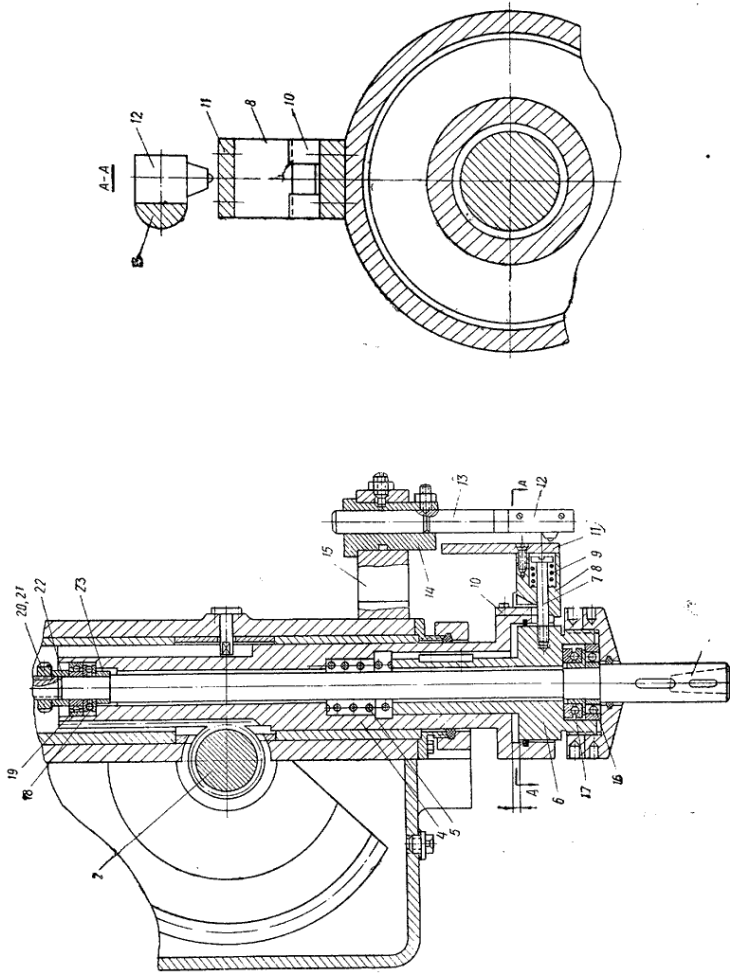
Механізм подачі шпинделя свердлильного верстата.[13]
